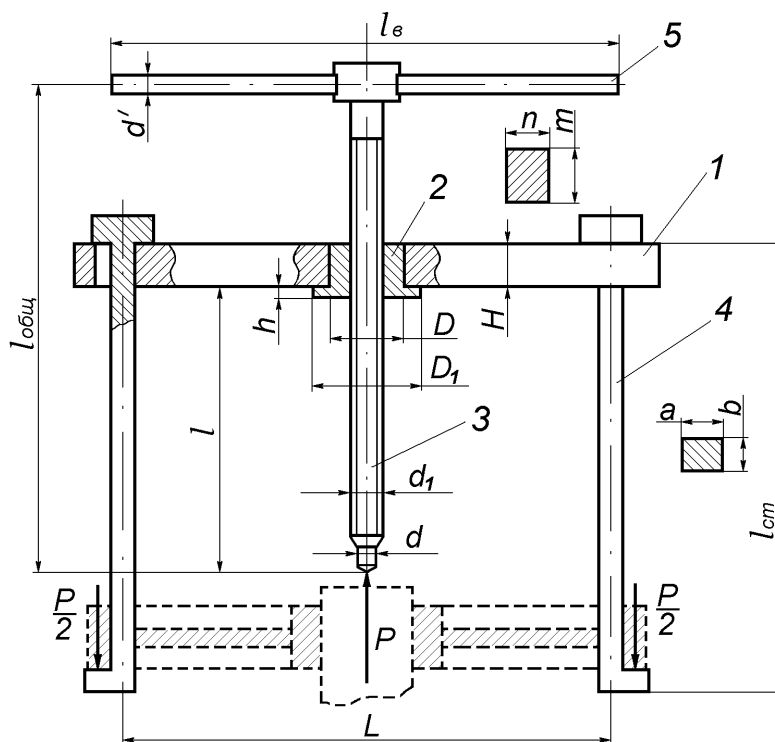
Эскиз съемника: 1 – балка; 2 – гайка; 3 – упорный винт; 4 – стойка в сборе с упорами; 5 – вороток
